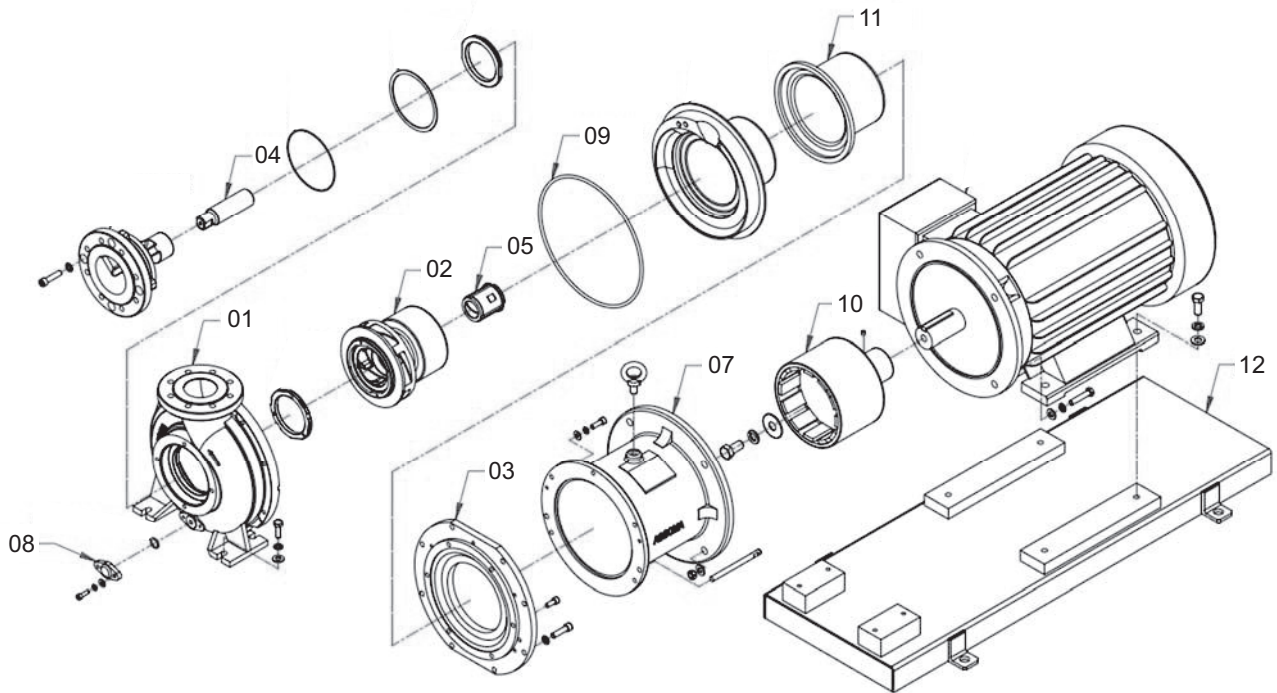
Teile (Explosionszeichnung), Baugröße 80 und 100
